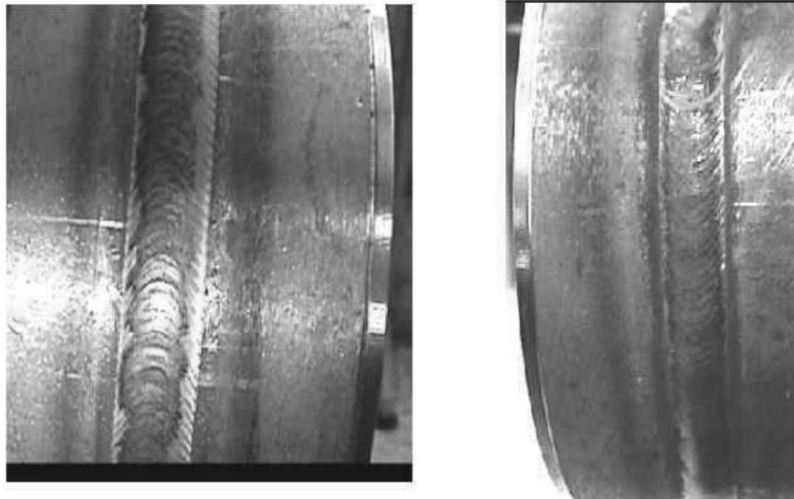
Зовнішній вигляд облицювального шару зварювального шва виконаного автоматичним регулюванням дуги саморегулювання
